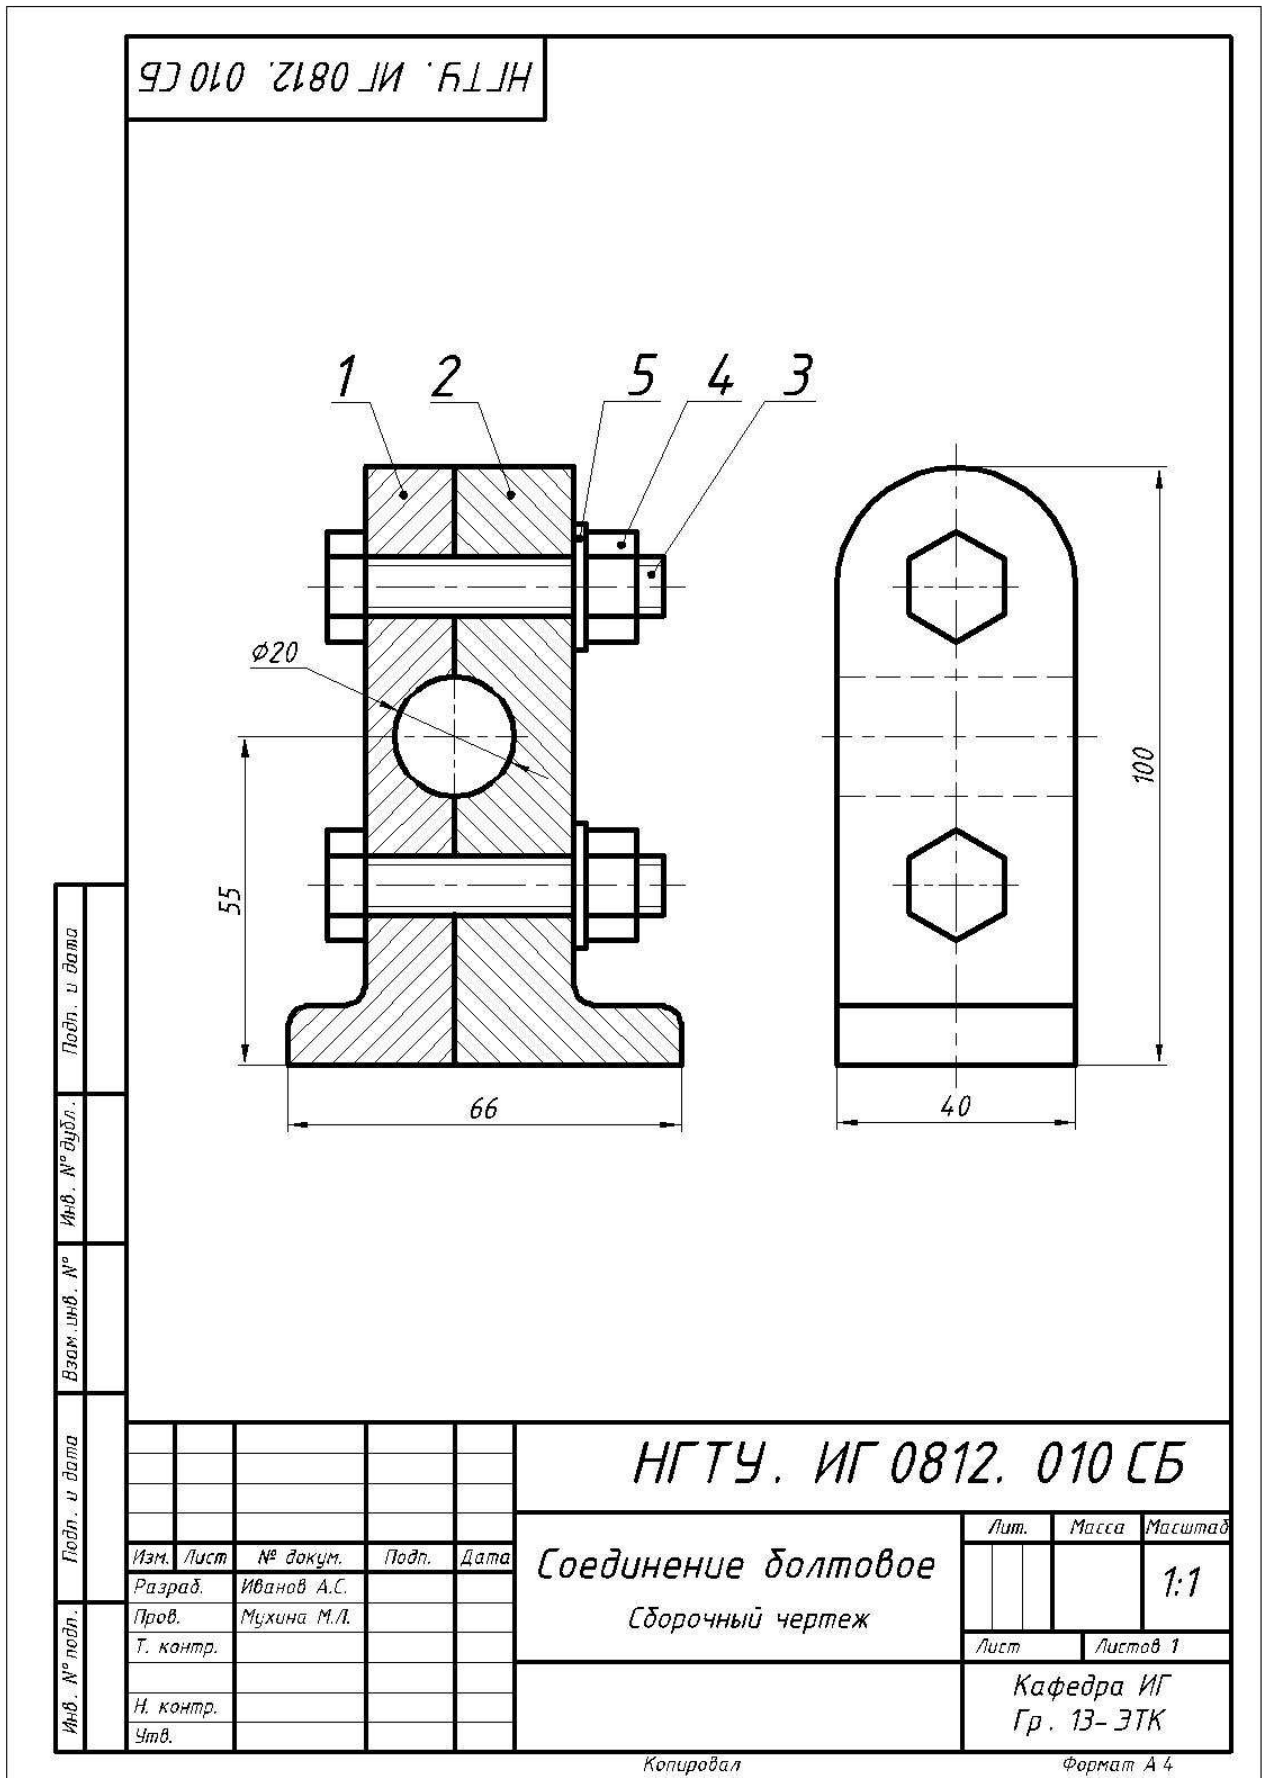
Образец выполнения чертежа «Соединение болтовое»
